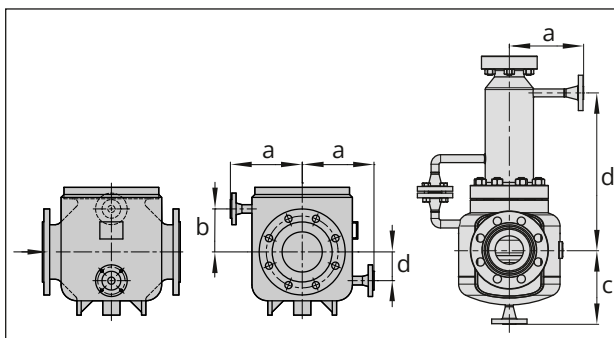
Typ 3251 med värmejacka · Dimensioner på begäran
